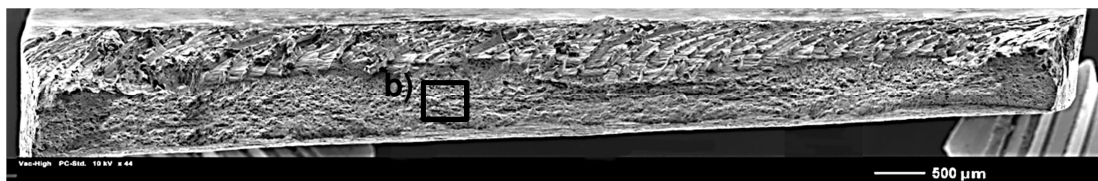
Übersichtsaufnahme der Bruchfläche der FSW-Verbindung ISF-22-00048
